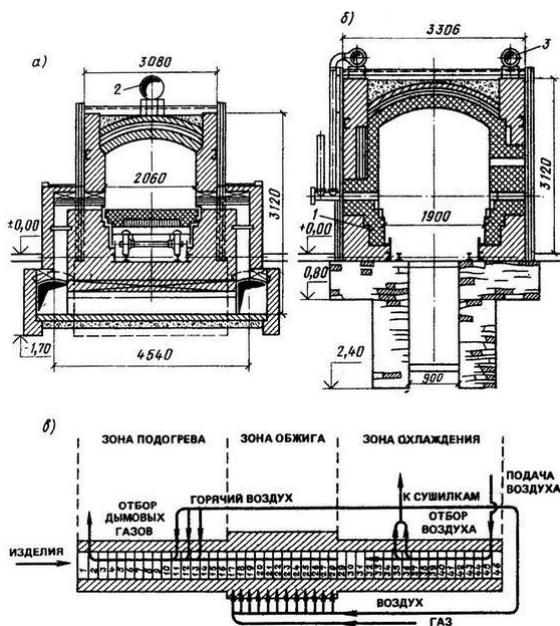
Туннельная печь Гипрострома (Киев): а – зона подогрева; б – зона взвара (1 – кладка печи; 2 – воздухопровод; 3 – газопровод); в – схема тепловых зон
